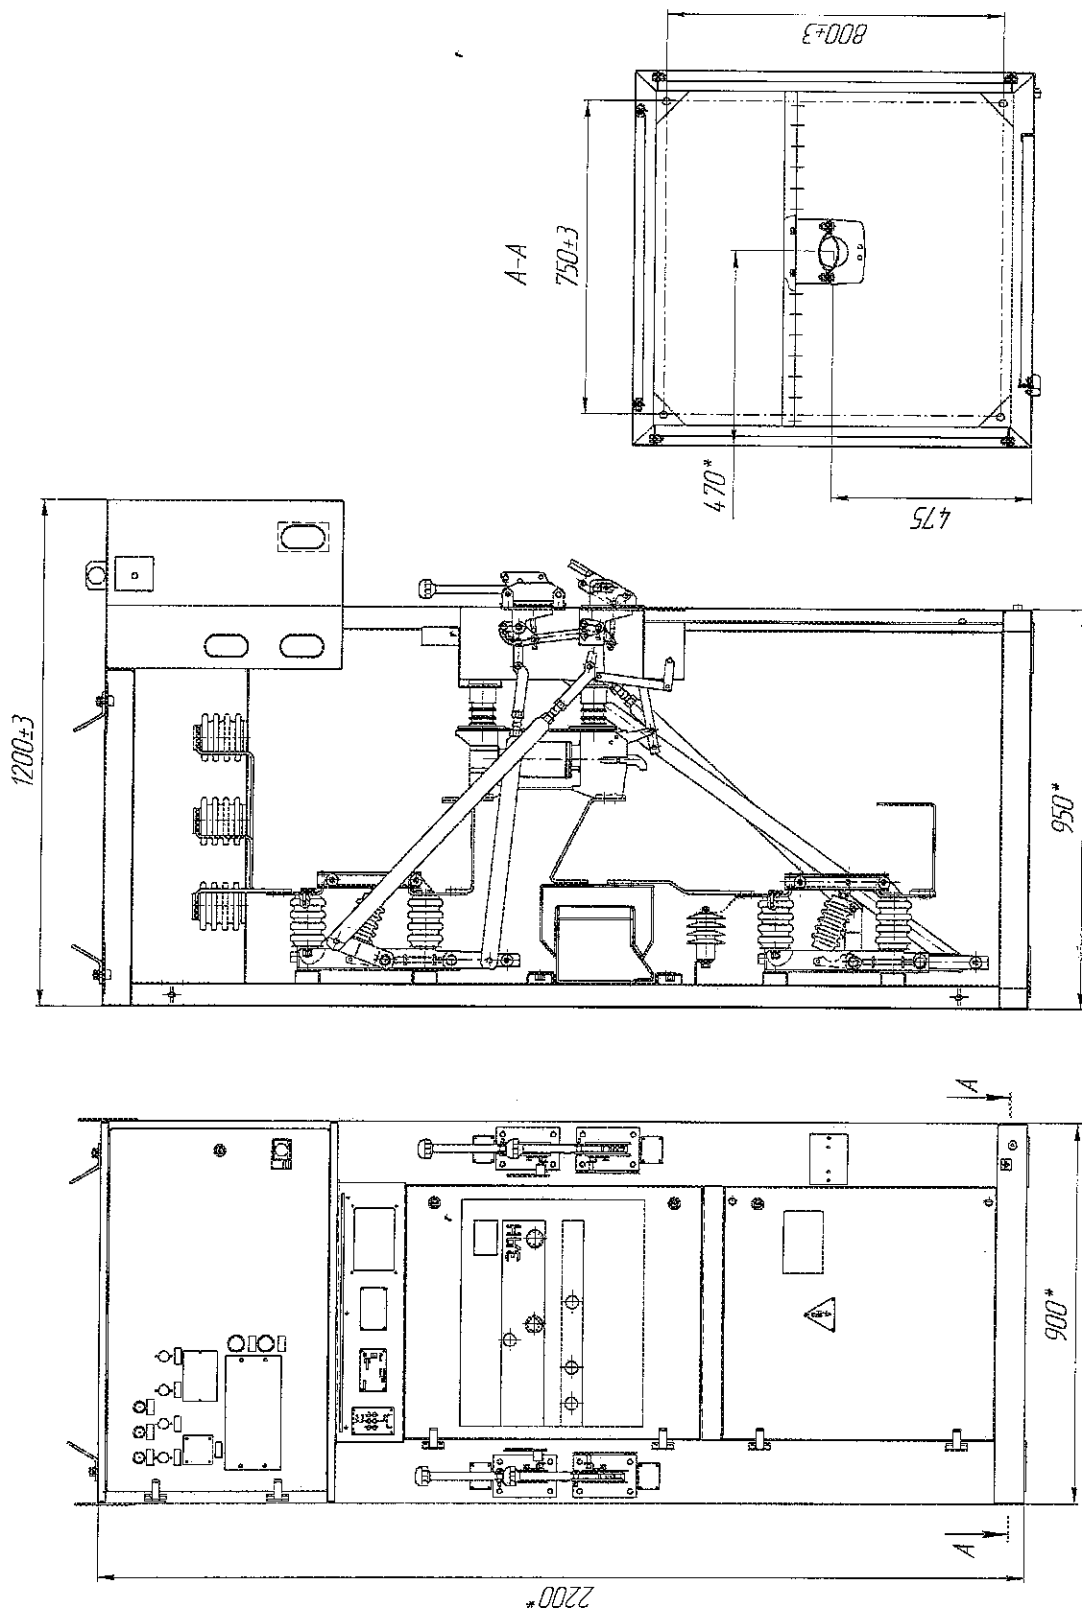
Габаритные, установочные, присоединительные размеры КСО-202ВМ с вакуумным выключателем Siemens.
